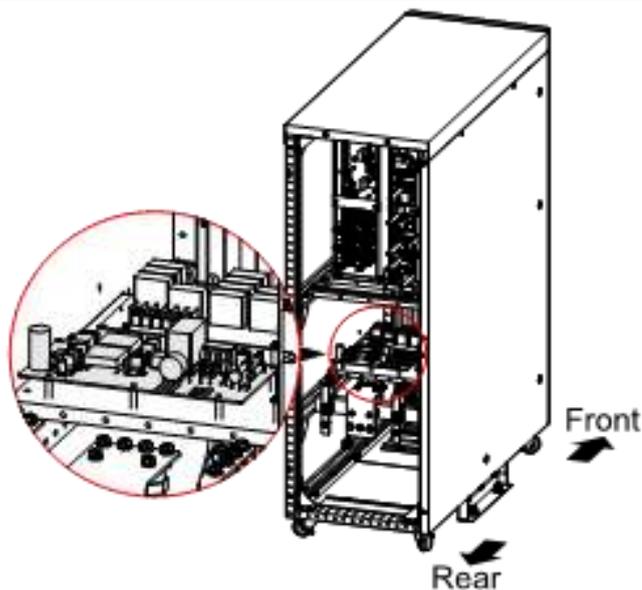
Установка платы устройства управления размыкателем цепи батареи МУ60, МУ80, МУ100, МУ120
